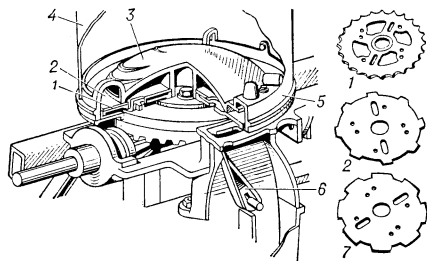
Ячеисто-дисковый высевающий аппарат: 1 — опорный диск; 2 — высевающий диск; 3 — крошштейн-днище; 4 — ведущий диск; 5 — семенная банка; 6 и 7 — ролики-выталькиватели.
